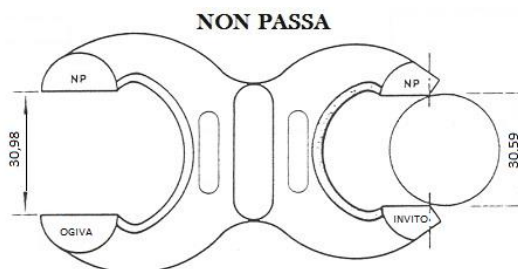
Calibro a forchetta del tipo “non passa”
